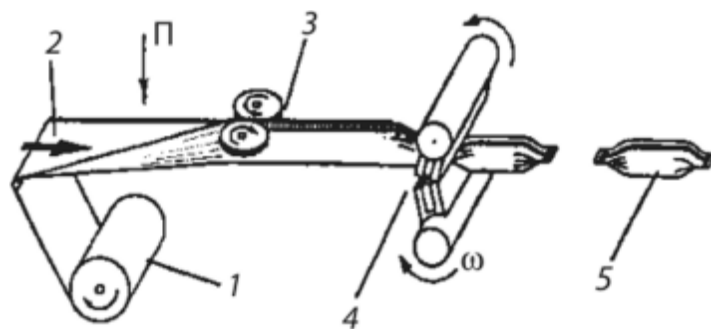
Сварка пленочной упаковки контактным нагревом
